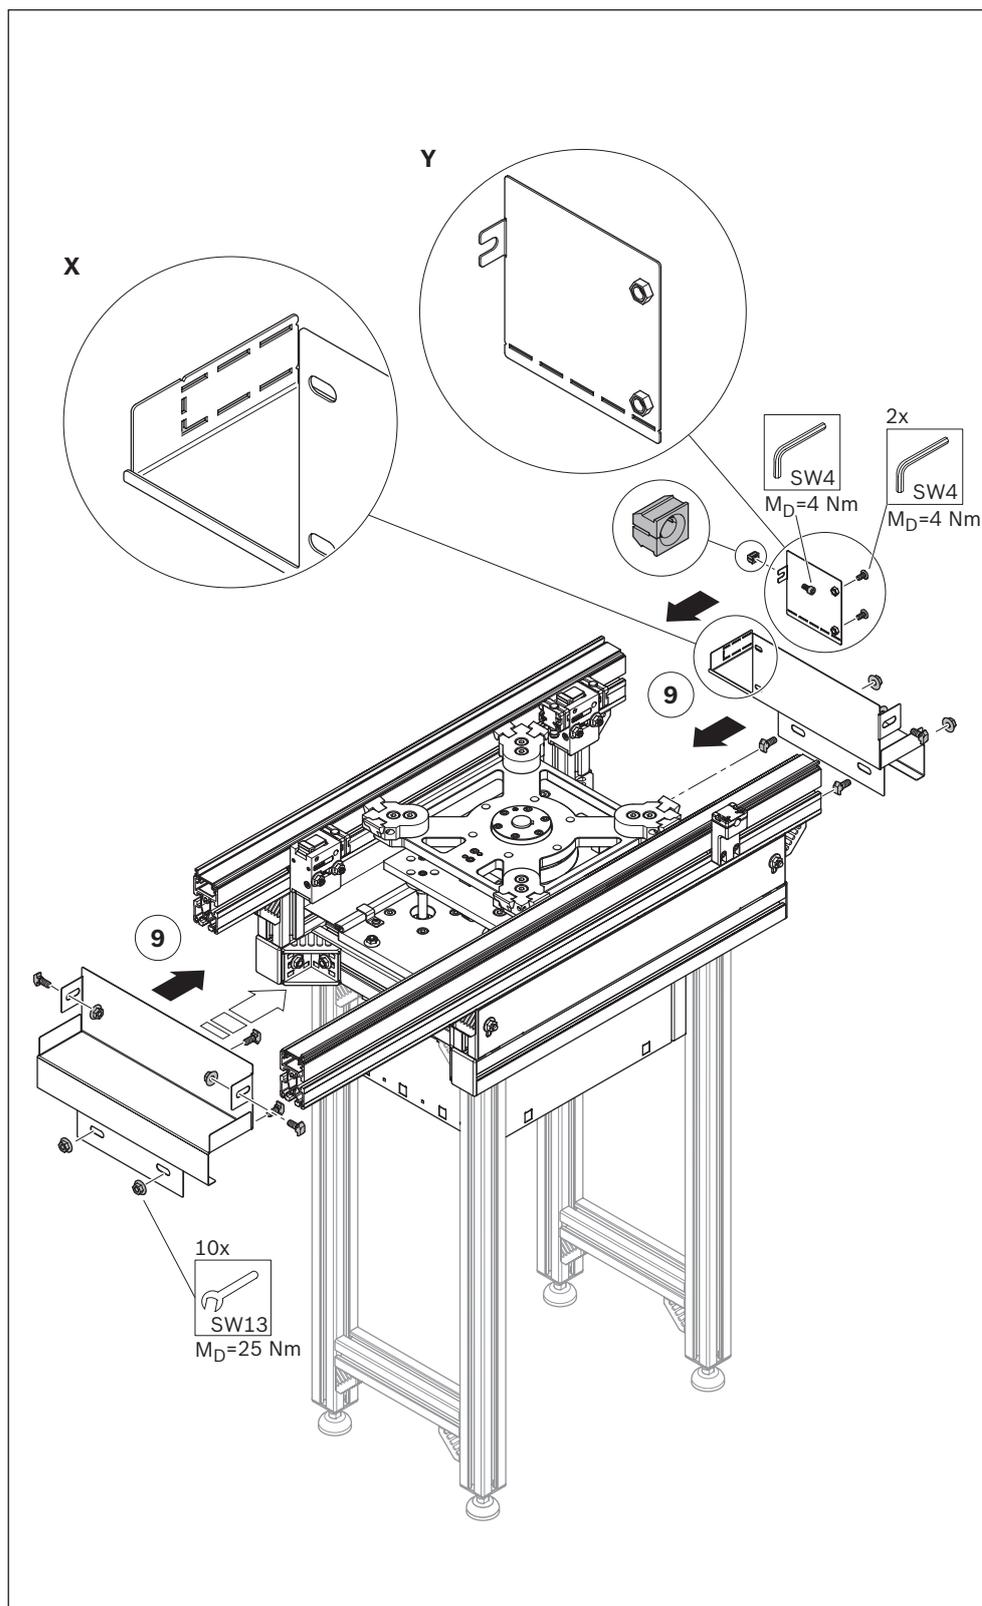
Montaggio di lamiere di protezione (nell'esempio, grandezza 2 180° per WT 2, WT 2/F)
